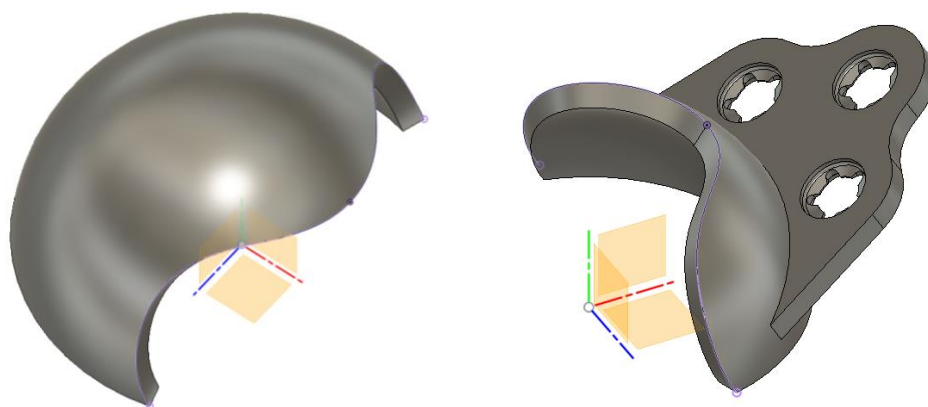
Отримуємо корпус та козирок імплантата
